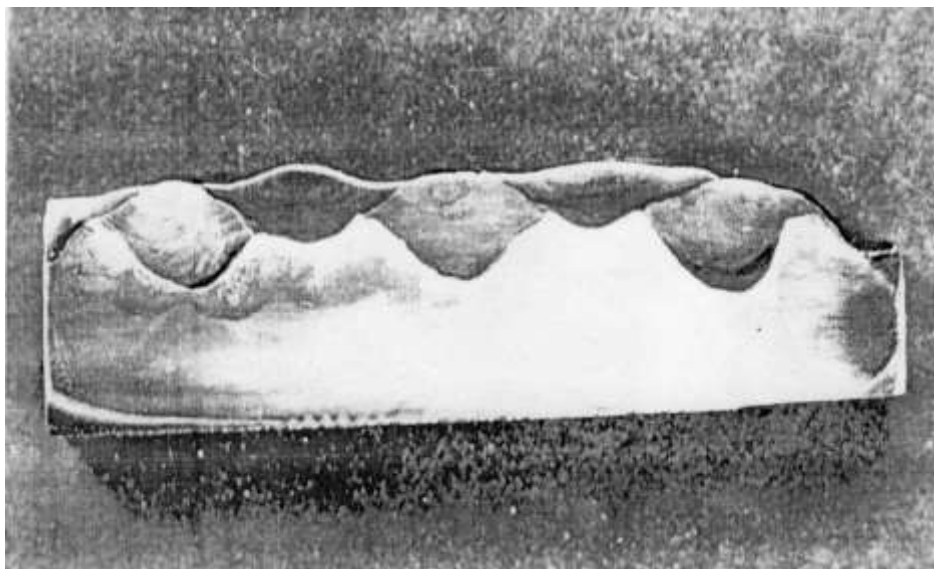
Микрошлиф многослойной наплавки порошковой проволокой ПП-АН-170
